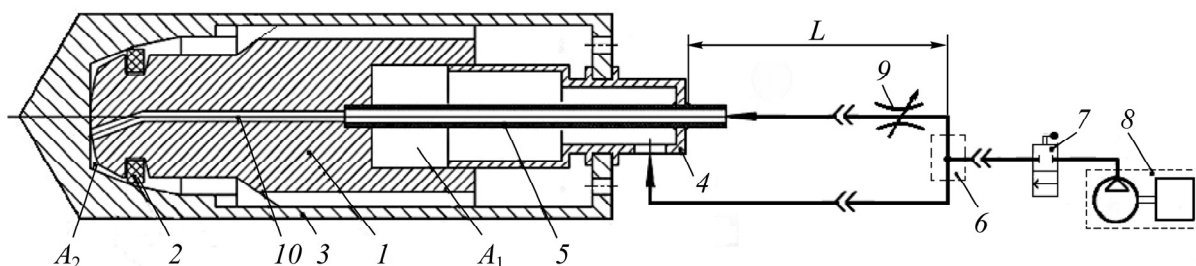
Схема экспериментального образца машины: 1 — ударник; 2 — кольцевой клапан; 3 — корпус; 4 — патрубок; 5 — гибкий воздуховод; 6 — распределительная коробка; 7 — пусковой кран; 8 — источник сжатого воздуха; 9 — дроссельный регулятор; 10 — центральный канал
